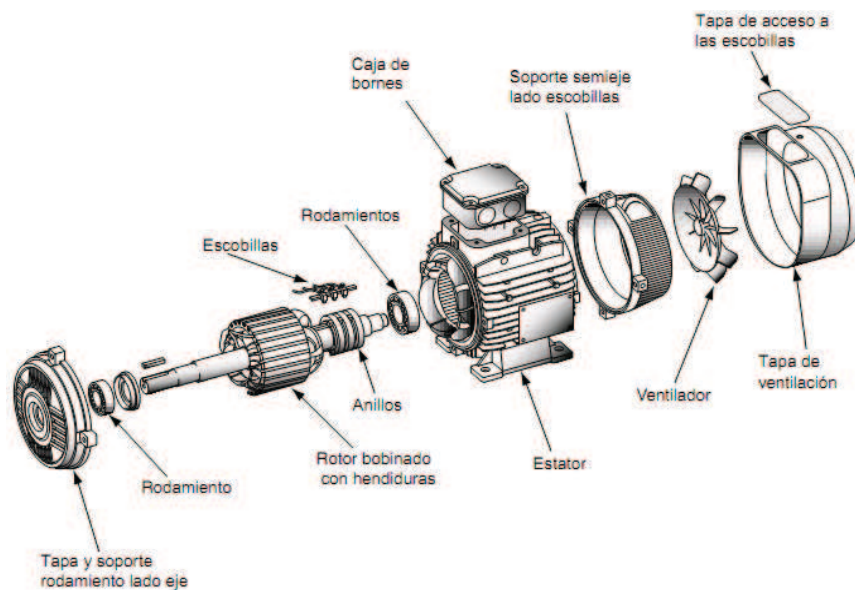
Partes motor trifásico asíncrono c.a. rotor bobinado
